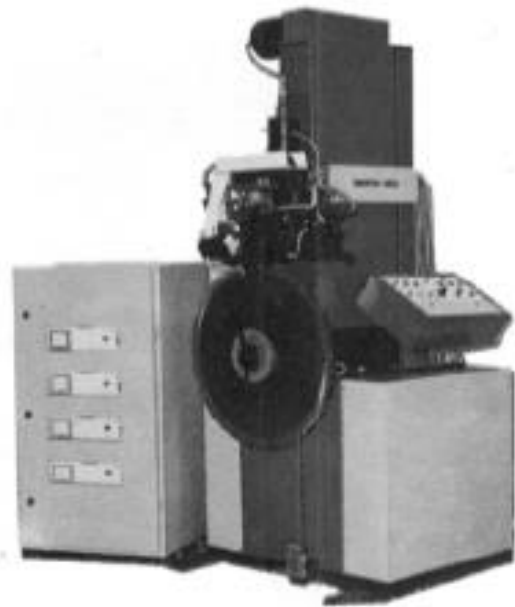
Внешний вид установки ЭЛИТРОН—345А
